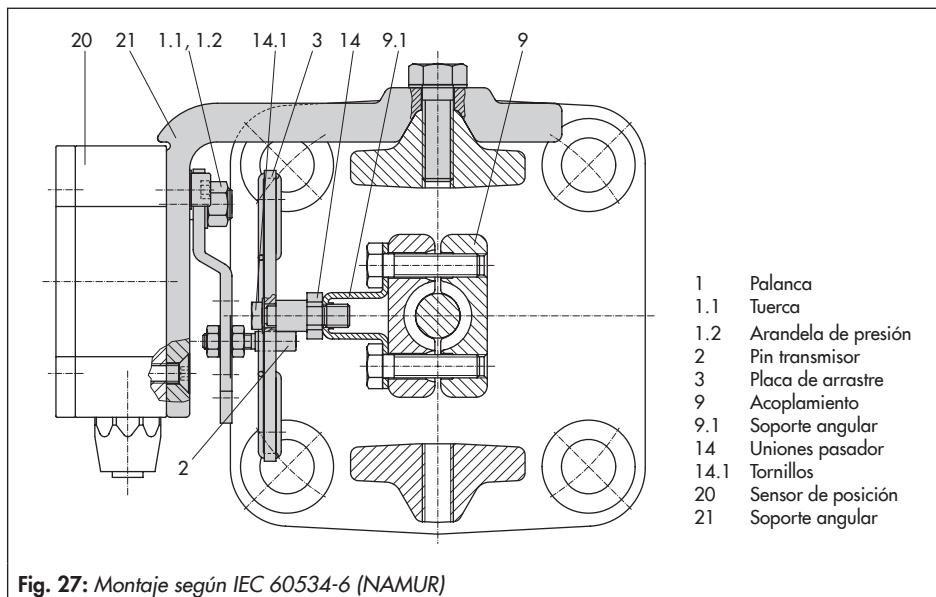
Montaje según IEC 60534-6 (NAMUR)
